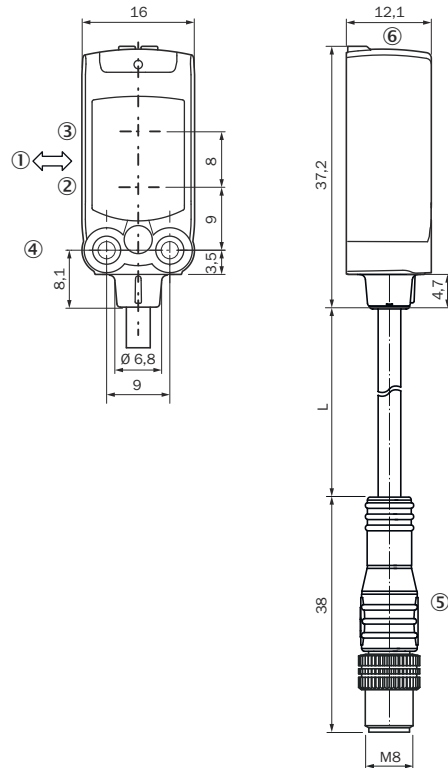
Maßzeichnung, Leitung mit Stecker M8, Rändelverschraubung
